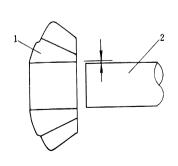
行星齿轮与行星齿轮轴间隙的检查
